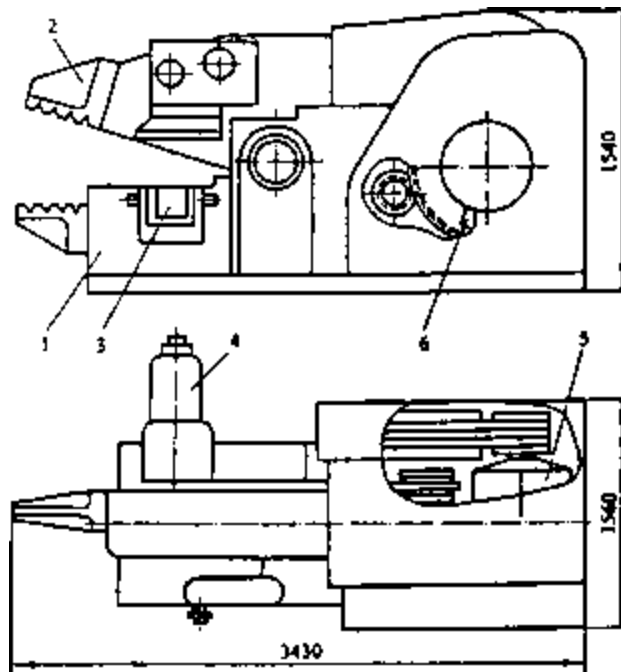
Алігаторні (важільні) ножиці : 1 - станина, 2 - щелепа, 3 - ролик, 4 - опора, 5 - привід; 6-запобіжний пристрій
